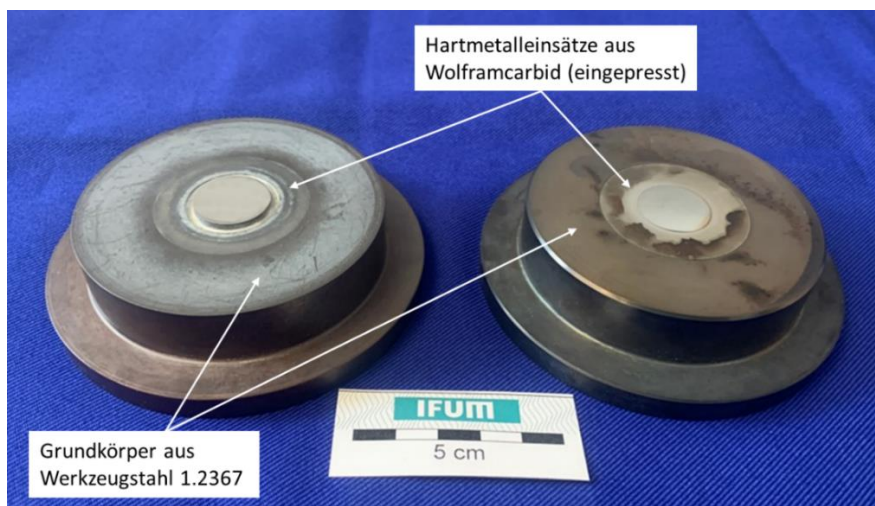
Werkzeuge für Umformversuche mit ein eingepressten Hartmetalleinsätzen aus Wolframcarbid
